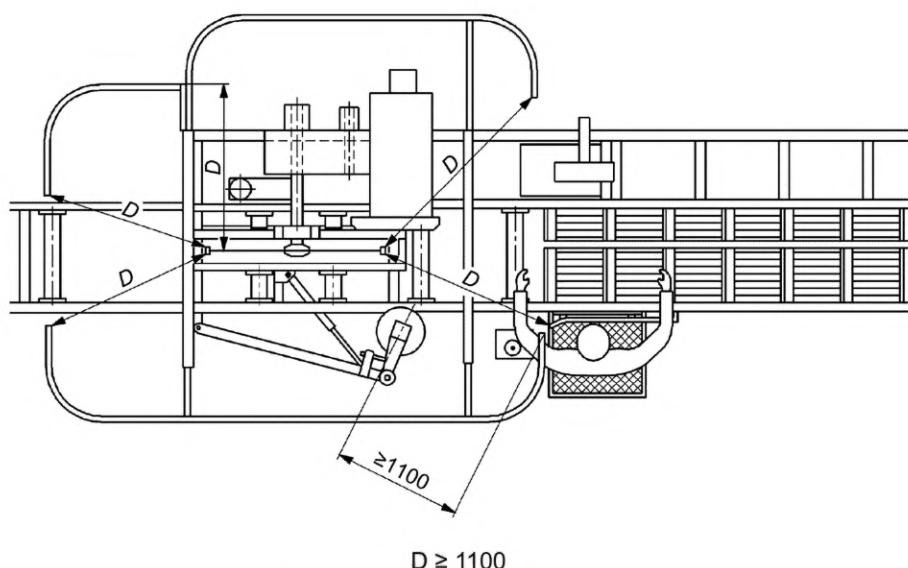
Пример защиты дисковой пилы (вид сверху)
